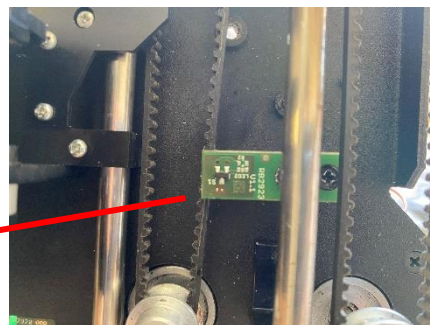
/ Photo du capteur qui a remplacé le capteur qui a brulé
